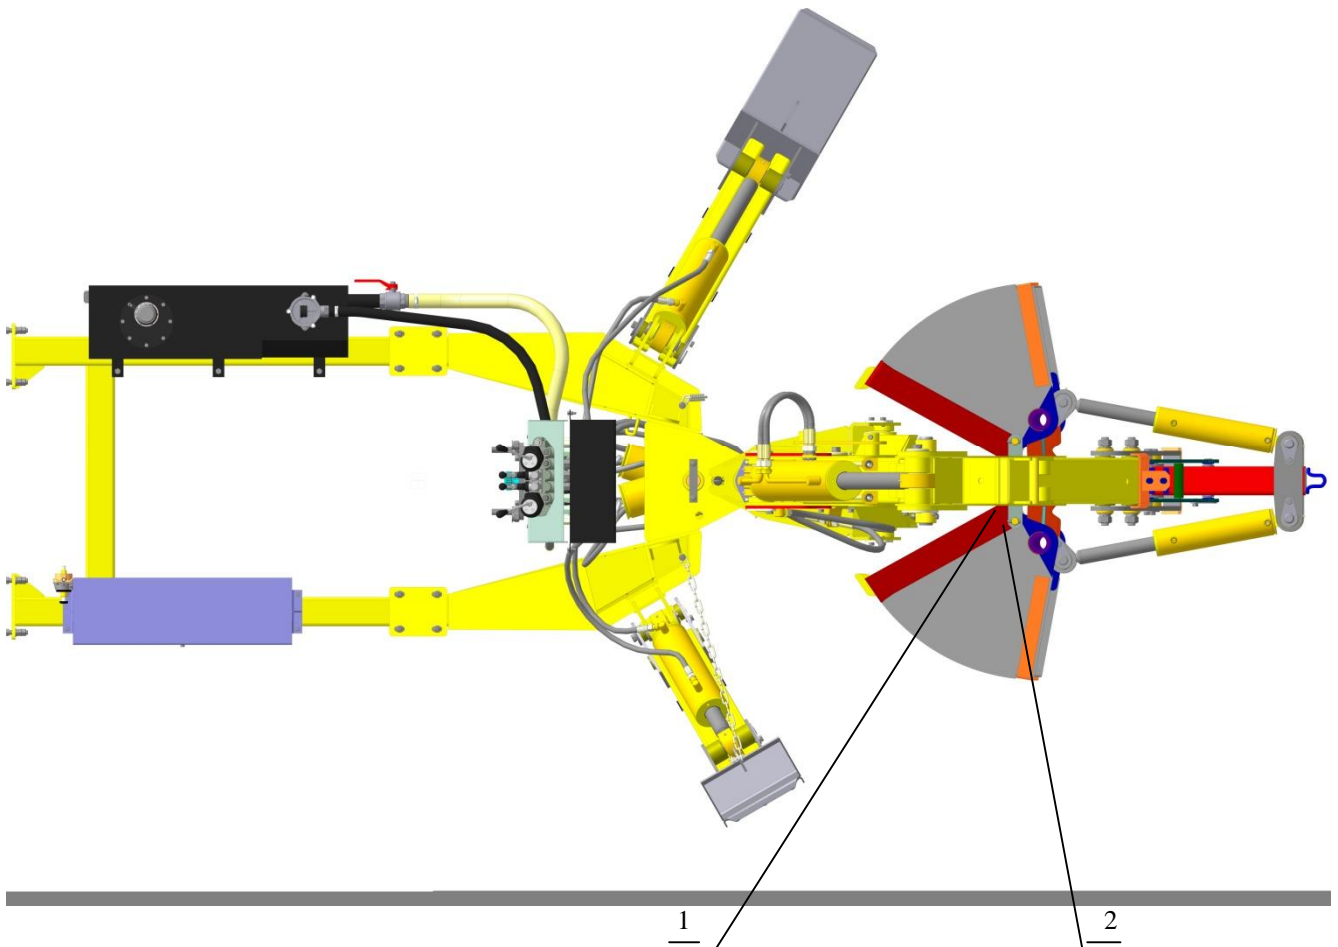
Приведения Ковшей грейферных Э-01-30 и Э-01-40 и Захвата грейферного Э-01-70 в транспортное положение (вид сверху).
